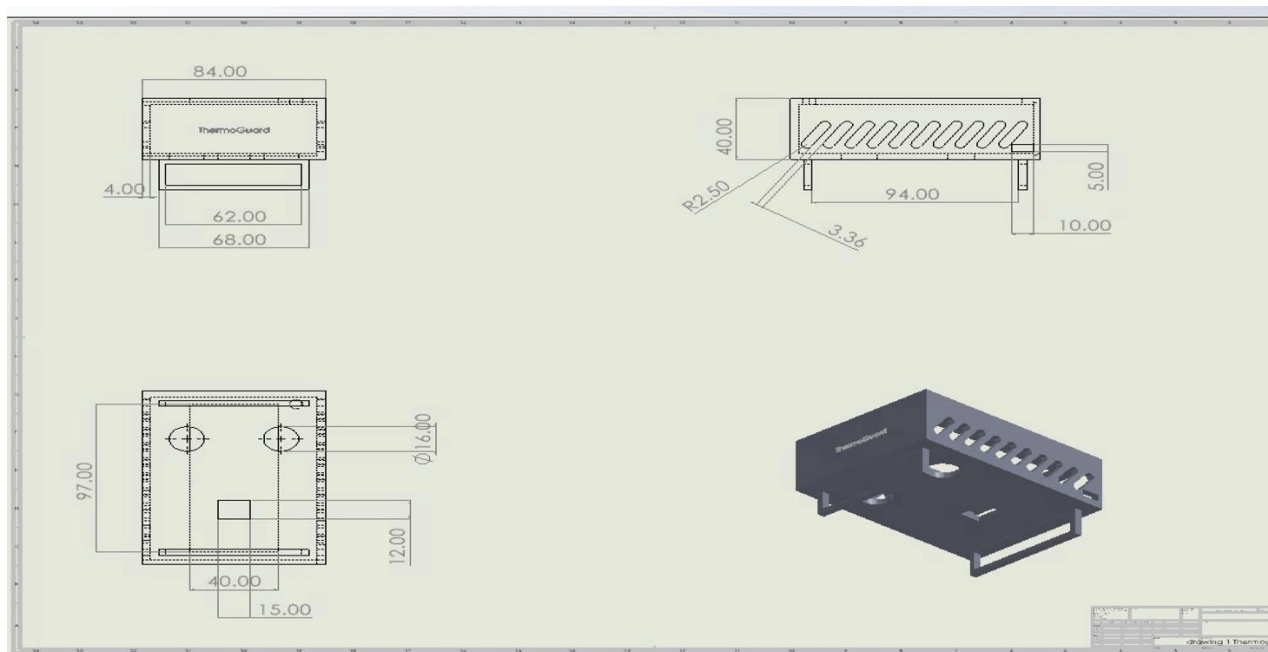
Dessin technique du boîtier avec dimensions et vue isométrique et orthogonale
